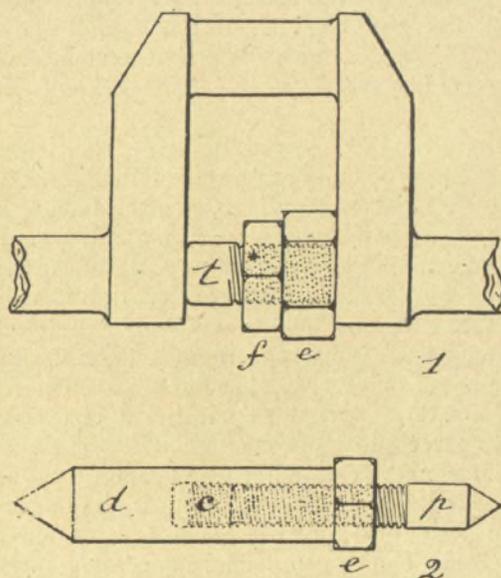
Entretoises extensibles pour l'usinage des arbres manivelle.
